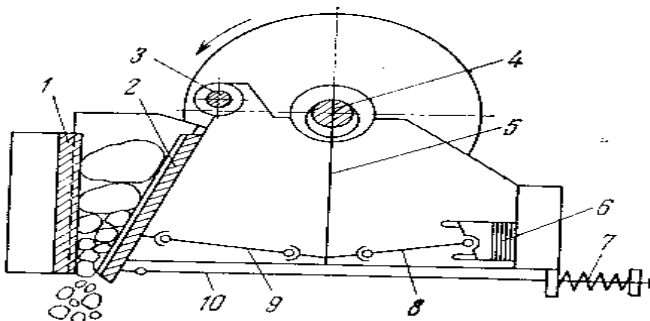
Схематическое изображение щековой дробилки с простым движением щеки: 1 - неподвижная щека; 2 - подвижная щека; 3 - ось подвески щеки; 4 - эксцентриковый вал; 5 - шатун; 6 - механизм изменения ширины выпускной щели; 7 - пружина; 8, 9 - распорные плиты; 10 - штанга
